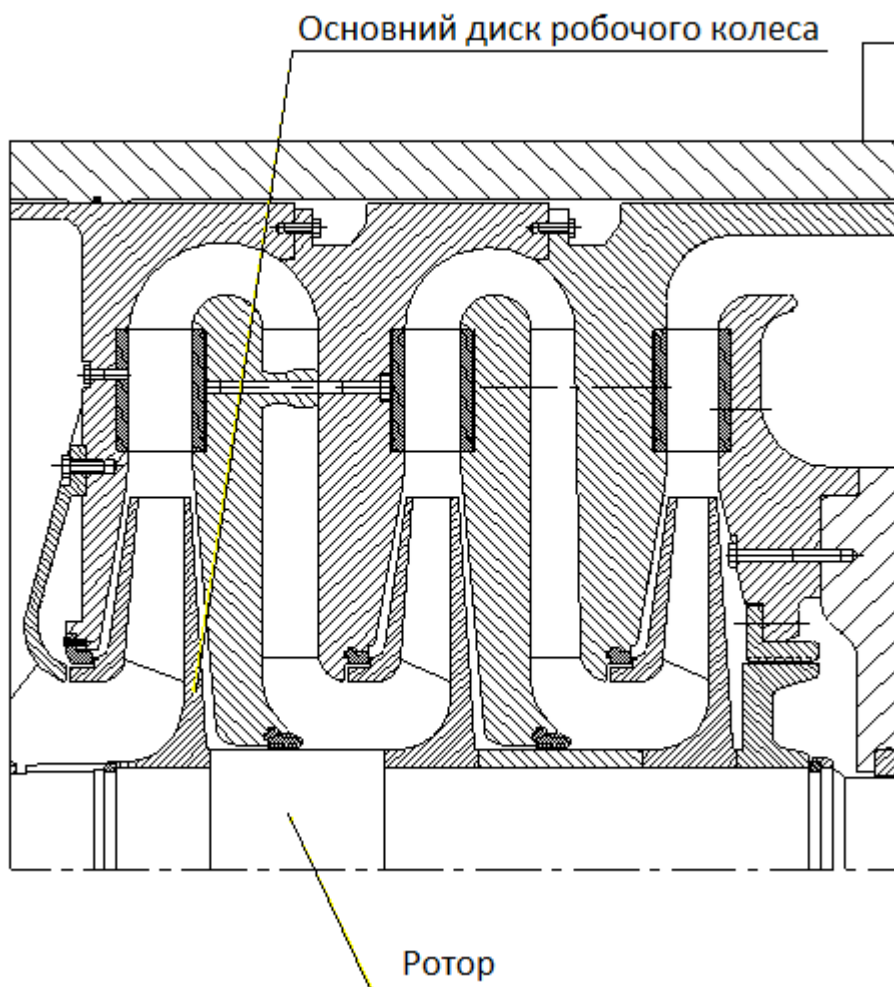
Ескіз розташування основного диску робочого колеса у відцентровому компресорі
